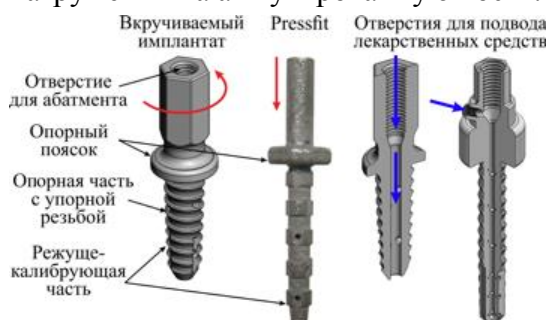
Типовые конструкции имплантатов для остеointegrации
